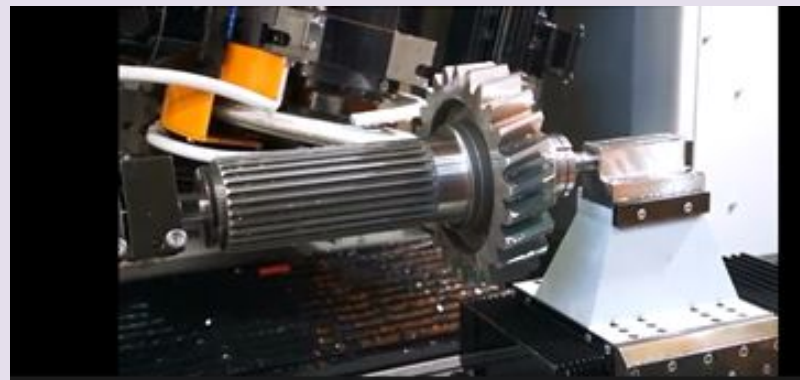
Процессы обработки прямозубой и косозубой шестерен на станке SMG 405 Stanexim
